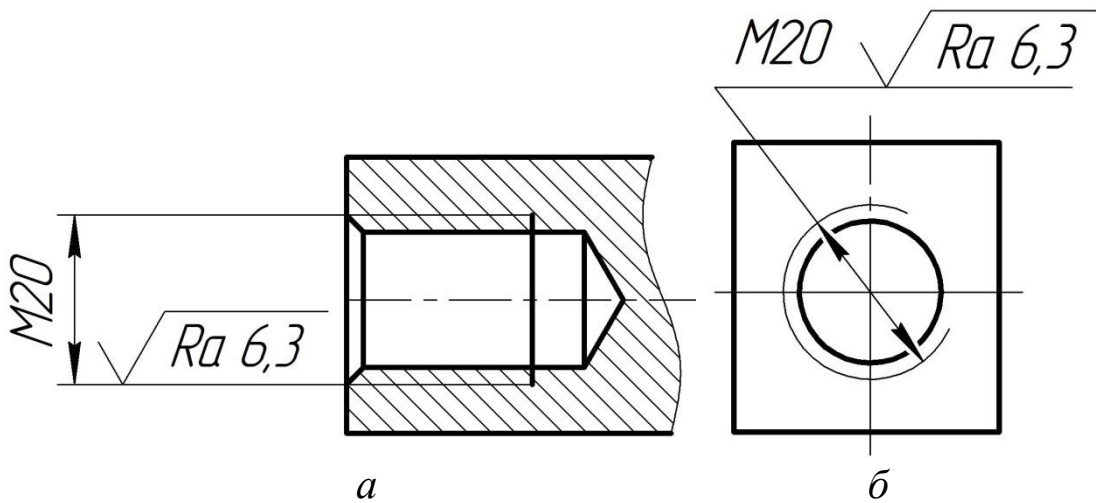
Обозначение шероховатости поверхности резьбы
